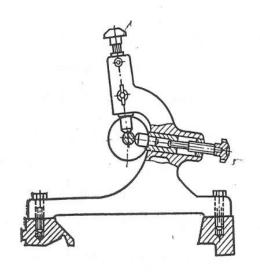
7 Подвижный люнет: 1 – винт; 2 – установочный винт
